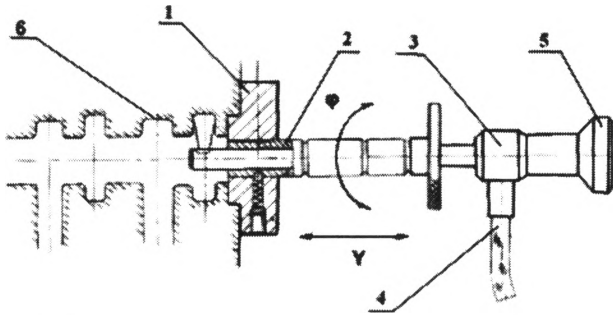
Схема установки визуального контроля: 1 – оправка; 2 – фиксатор положения; 3 – жесткий эндоскоп; 4 – осветительный жгут; 5 – объектив; 6 – отливка
